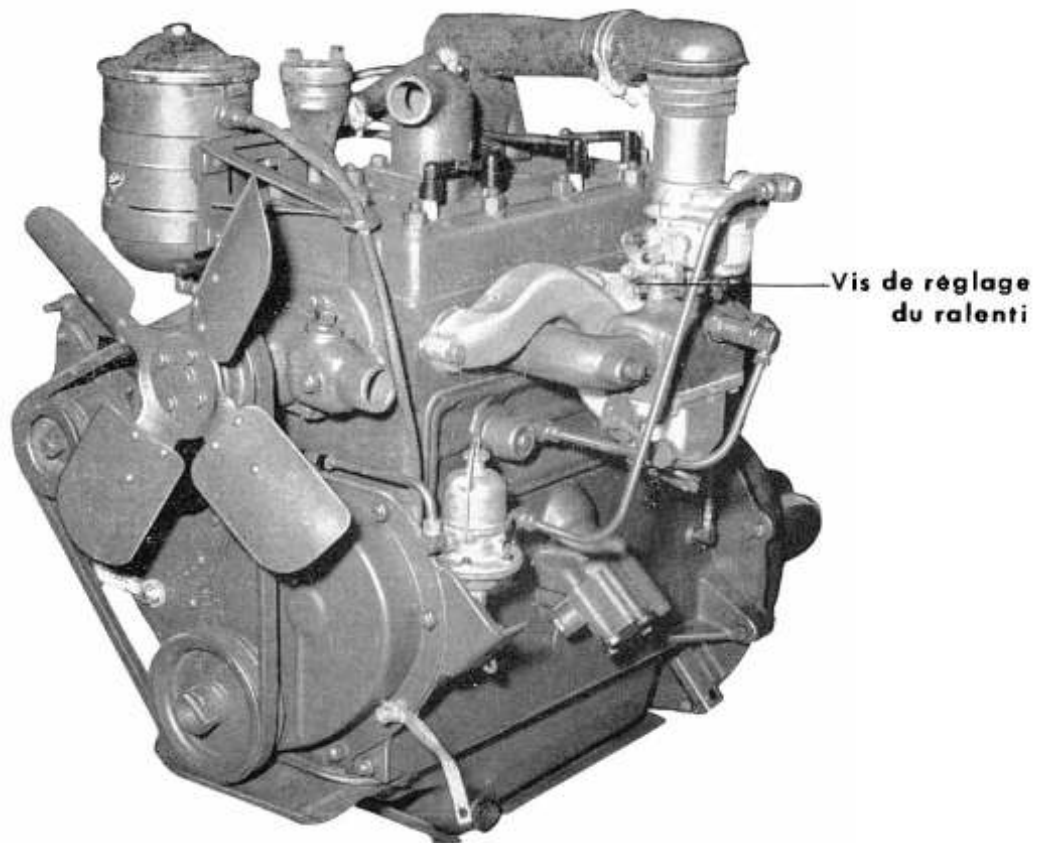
Vue de trois-quarts avant du moteur assemblé.
